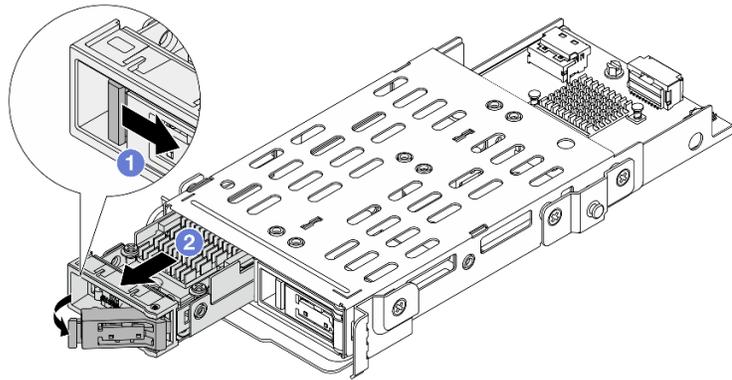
Entfernen der hinteren M.2-Laufwerkbaugruppe
